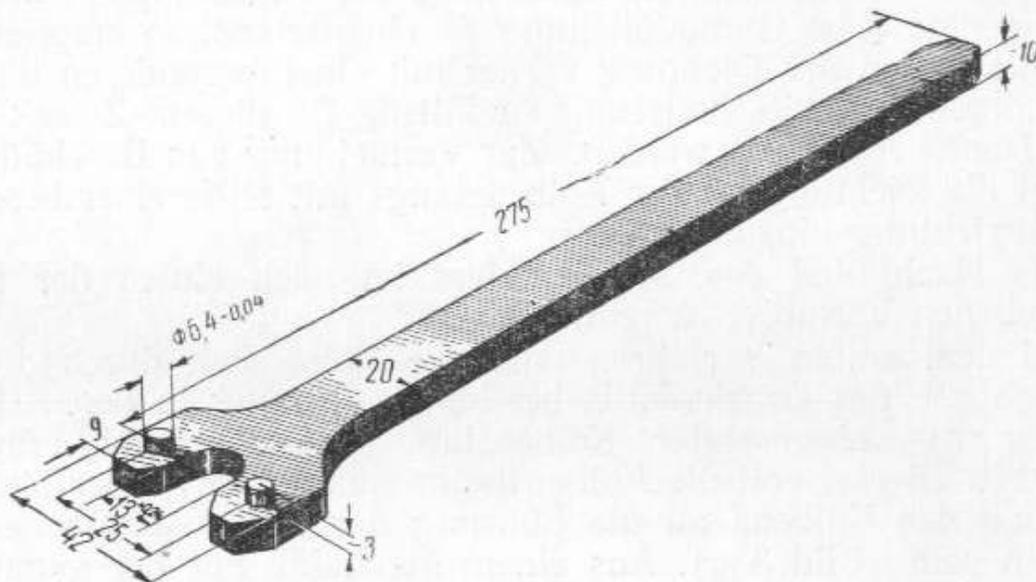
Sonderschlüssel für Ausbau des Stoßdämpfers
